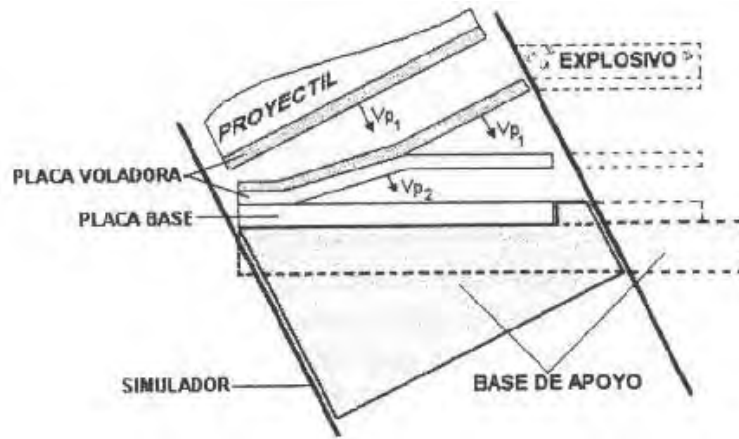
Relación entre la soldadura por explosión e impacto.
